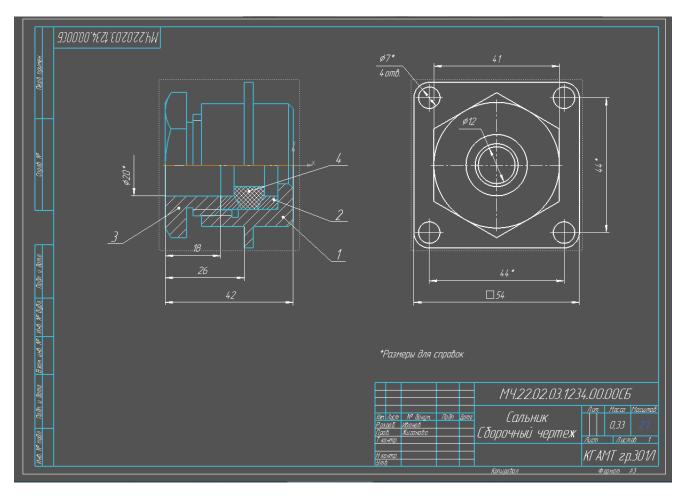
Оформление сборочного чертежа сальника на основе модели
